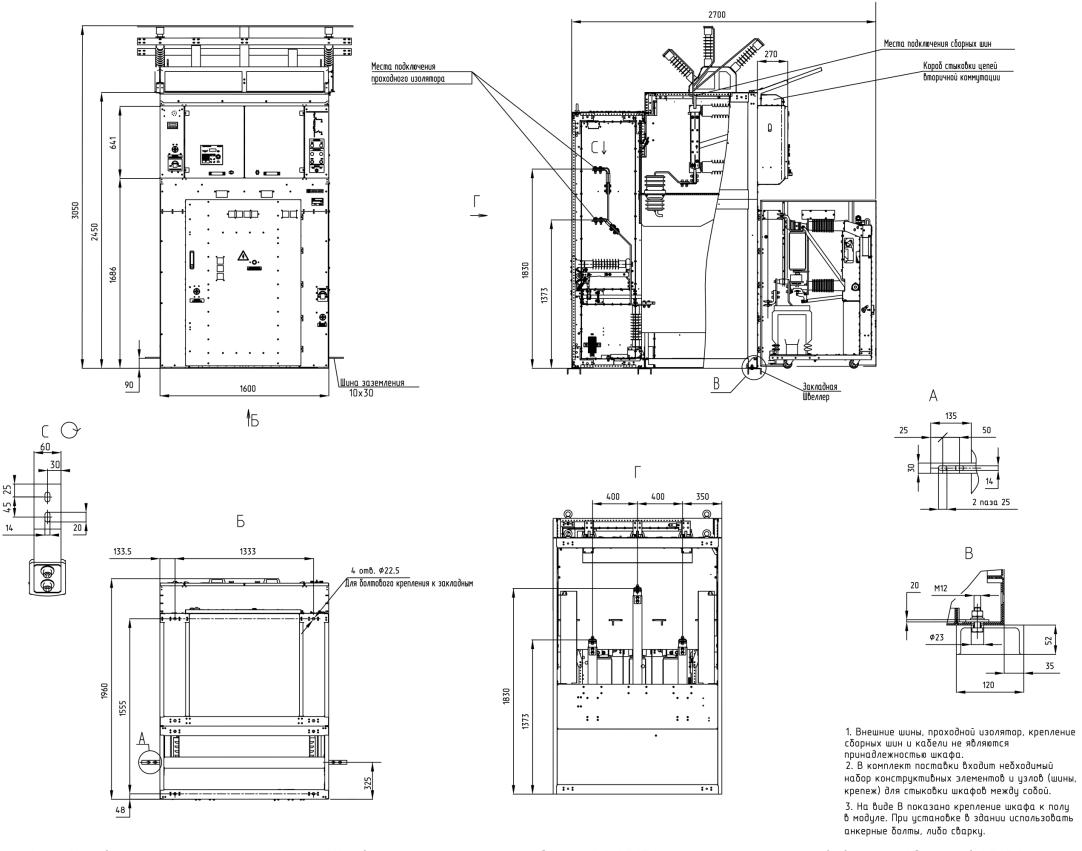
Шкафы с шинным подключением: Шкаф выключателя ввода 1С-35-3-ВВ-УХЛ4 номер схемы 01; шкаф фидера 1С-35-3-Ф-УХЛ4 номер схемы 02; шкаф выключателя ПВА 1С-35-3-ПВА-УХЛ4 номер схемы 03; шкаф выключателя ТСН 1С-35-3-ТСН-УХЛ4 номер схемы 04, масса – не более 1750 кг.
